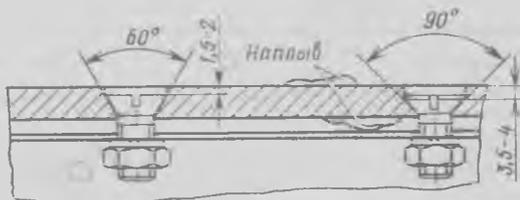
Напыль материала пропитки. Закрепление пластин различными винтами
